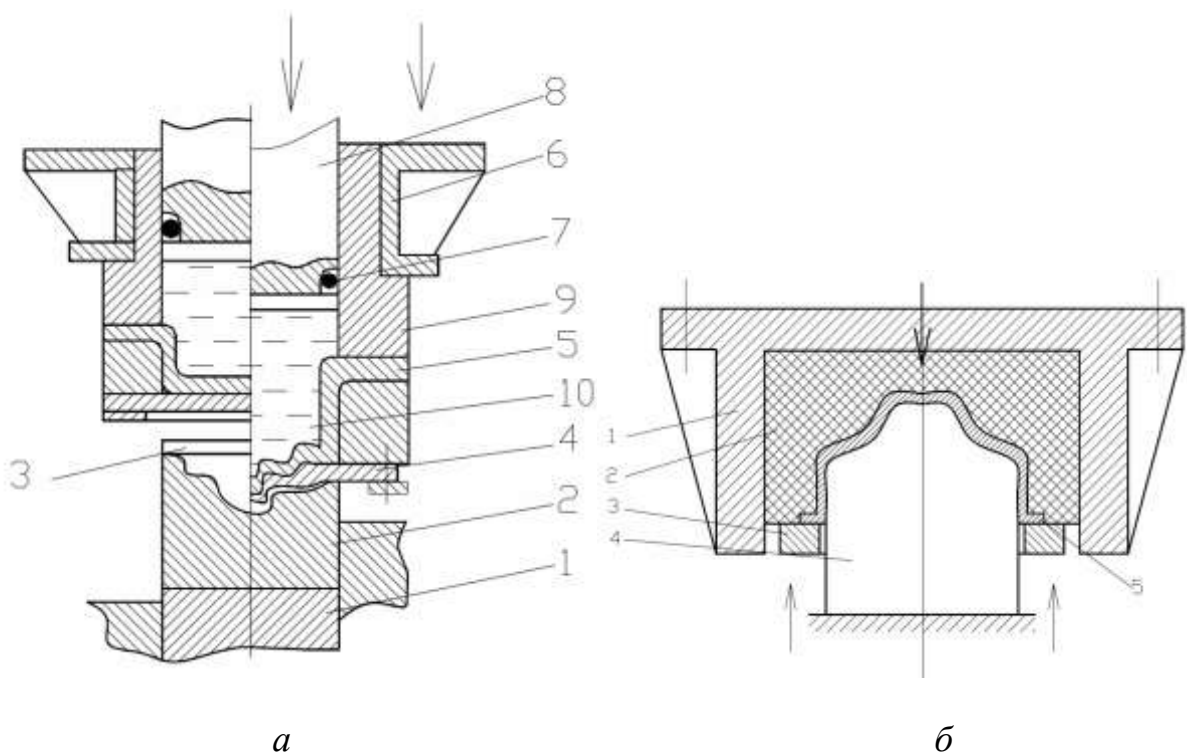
Схема процесу гідромеханічної витяжки (а) та типові деталі, що виготовляються витяжкою (б)
